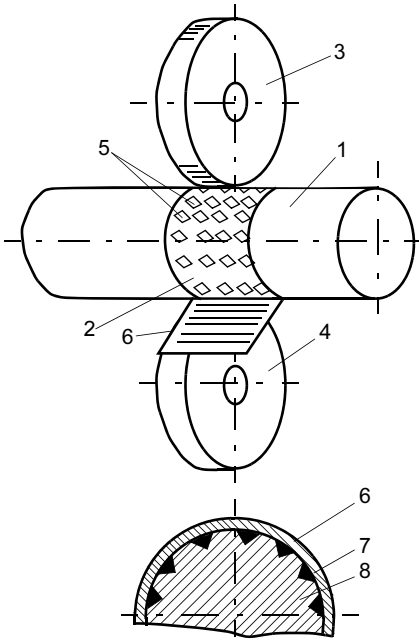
Существующая схема восстановления изношенных поверхностей: 1 — деталь; 2 — изношенная поверхность; 3, 4 — сварочные ролики; 5 — ячейки насечки; 6 — лента; 7 — впадины с припоем; 8 — гребни
